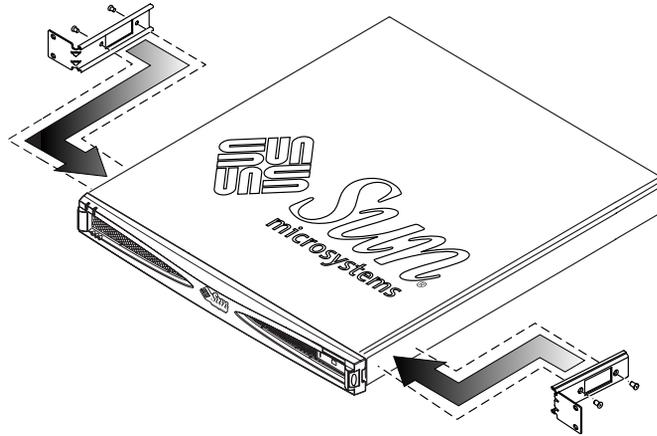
Fissaggio delle staffe di montaggio in rack verso la parte anteriore
